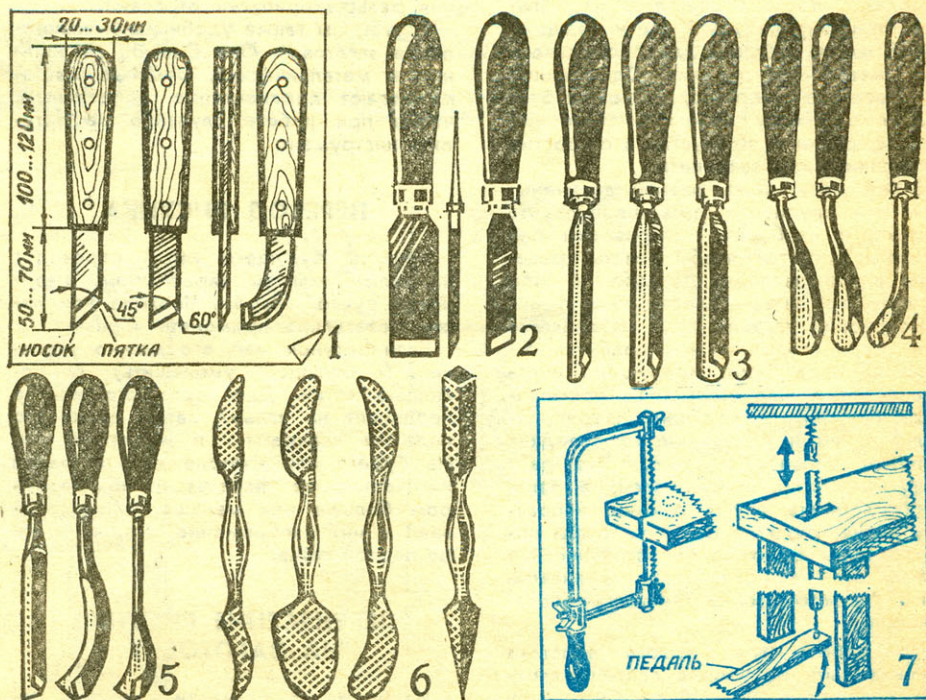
Инструменты для резьбы: 1 — ножи-косычки, 2 — стамески плоские, 3 — стамески полукруглые, 4 — клюкарзы, 5 — стамески уголкового, 6 — рашпили, 7 — лобзики (ручной и ножной).
